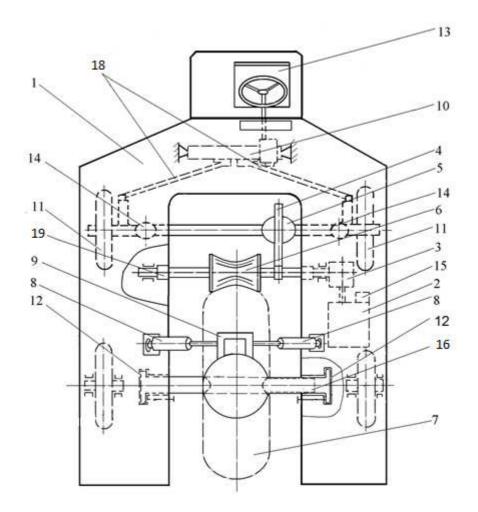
Малогабаритное буксировочное устройство. Вид сверху: 1 – несущая рама; 2 – двигатель (силовой агрегат); 3 – редуктор; 4 – привод управляемых ведущих колес буксировочной тележки; 5 – дифференциал; 6 – ведущий ролик привода колес воздушного судна; 7 – колесо воздушного судна; 8 – механизм догрузки; 9 – упор передней стойки самолета; 10 – рулевой механизм; 11 – управляемые ведущие колеса буксировочной тележки; 12 – механизм фиксации буксировочной тележки к передней стойке шасси воздушного судна; 13 – сидение водителя; 14 – шарниры равных угловых скоростей; 15 – гидравлический насос с распределителем; 16 – выдвигающийся палец; 18 – рулевая тяга; 19 – соединительная муфта
